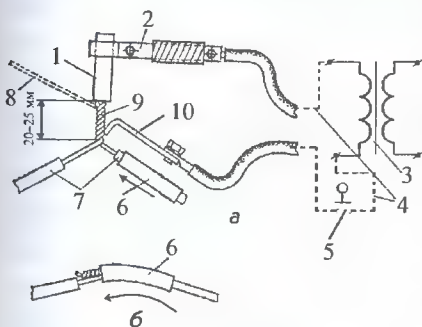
Сварка (а) и изолировка (б) соединений проводов
